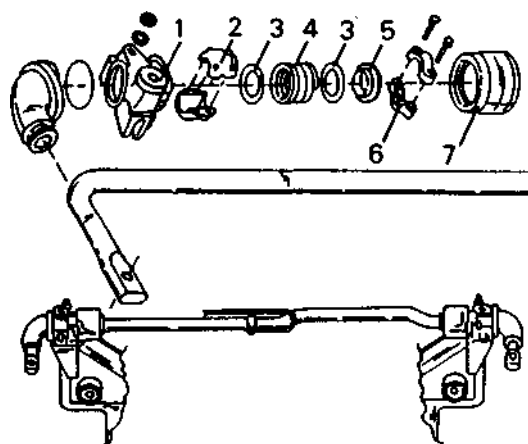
Sestava přední nápravy a zavěšení předních kol
